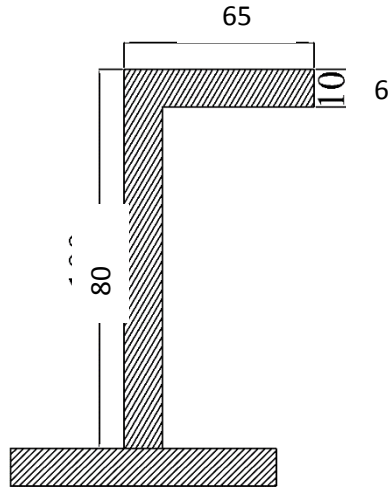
Panjang tak ditumpu *frame* pada haluan
